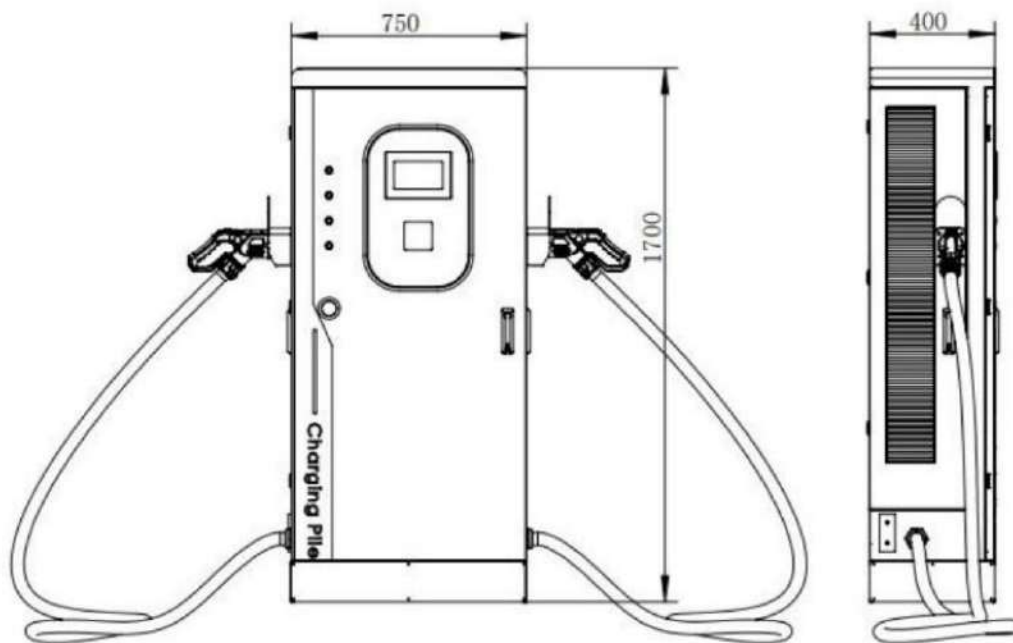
Dimensiones del equipo (MDDC-60kW/80kW)
